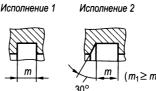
Канавка под упорное кольцо в корпусе
